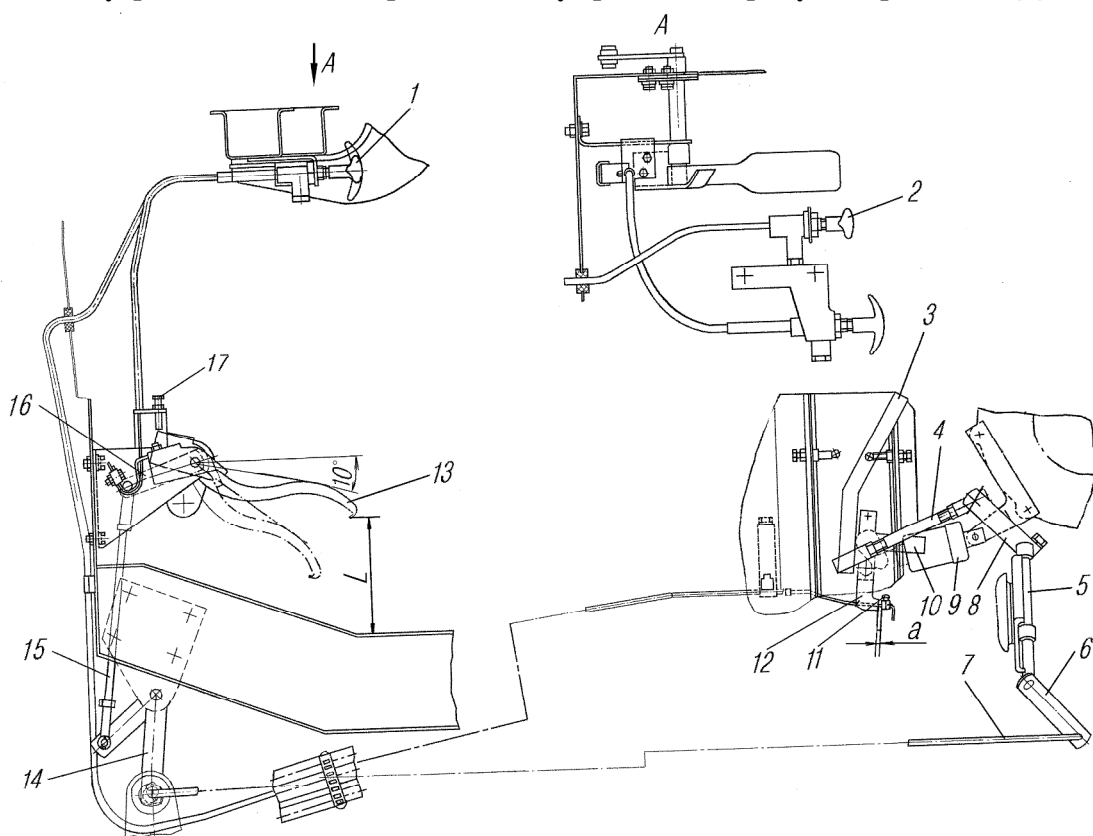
Привод управления подачей топлива и ручного останова двигателя:
